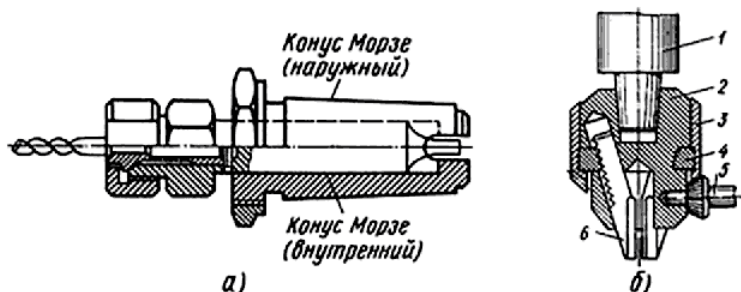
Сверло с переходной втулкой (а), патрон (б)
